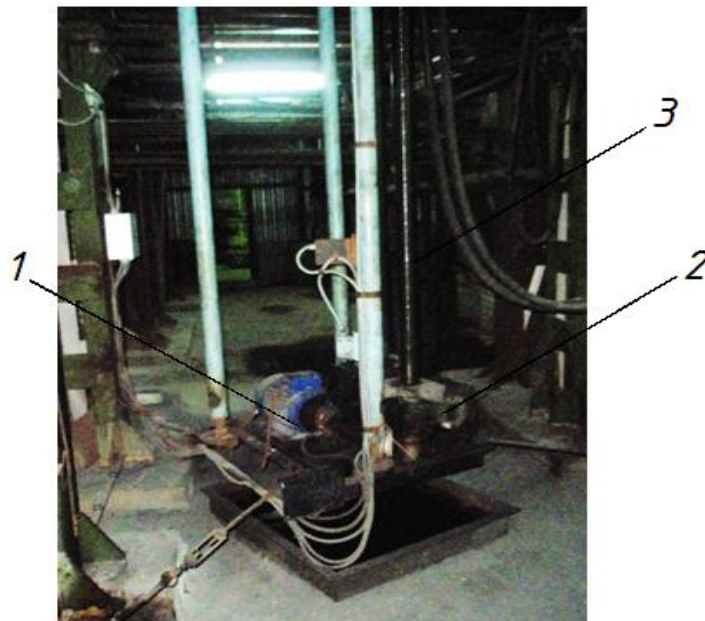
Привід витягування зливку з кристалізатора: 1 – електродвигун; 2 – редуктор; 3 – гвинтова передача
